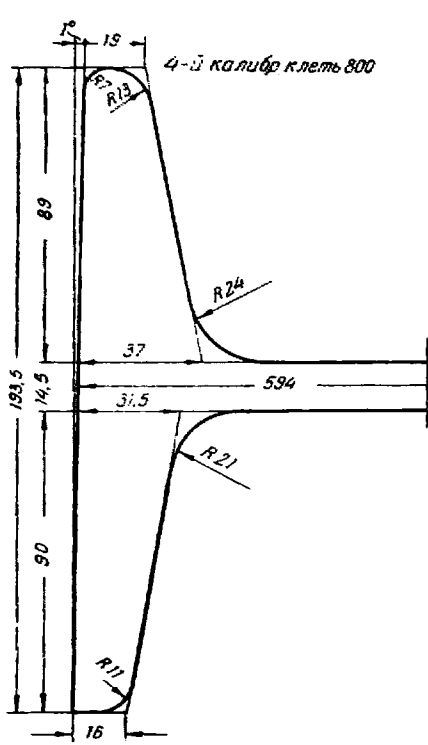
Продолжение. Калибровка валков для прокатки балки № 60
